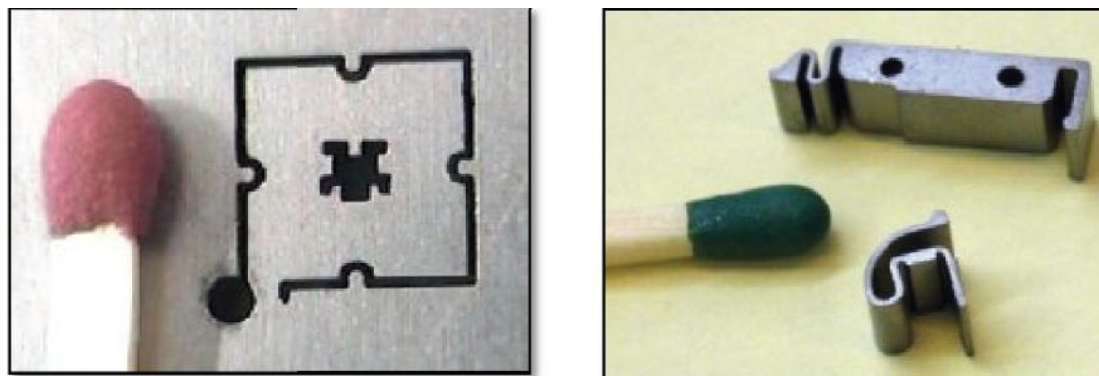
Quelques pièces usinées le découpage par fil [10].
